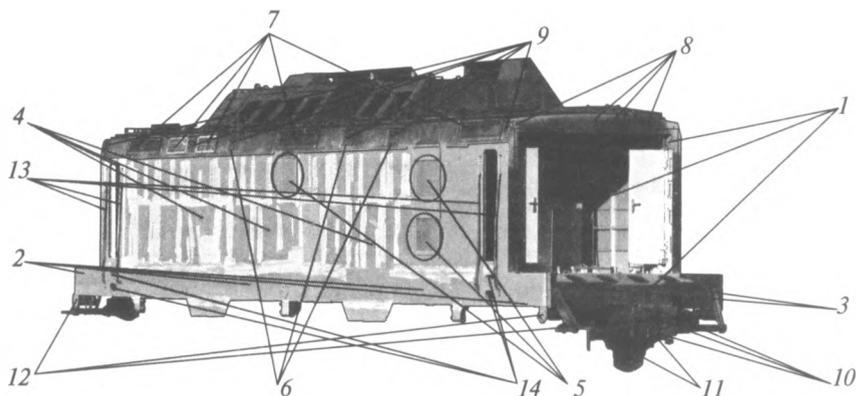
Несущая рама кузова электровоза неохватывающего типа:
